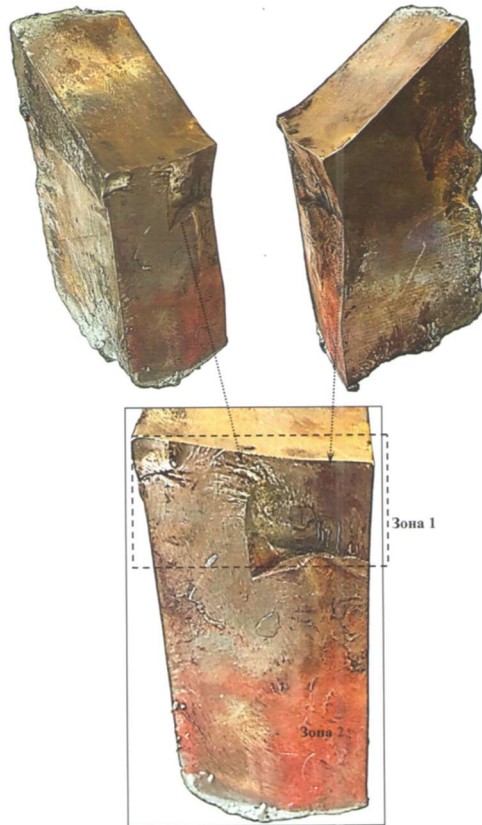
Внешний вид фрагмента разрушившегося нижнего ножа кривошипно-шатунных ножниц горячей резки и поверхности излома
